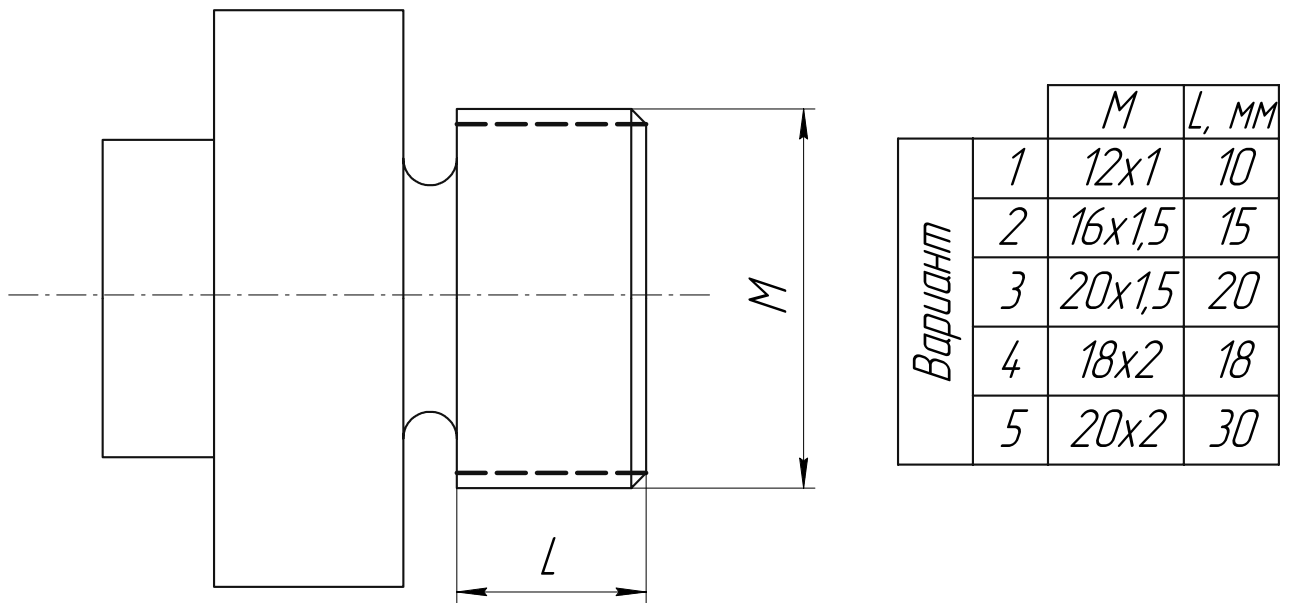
Нарезание резьбы резцами, гребенками и фрезами
